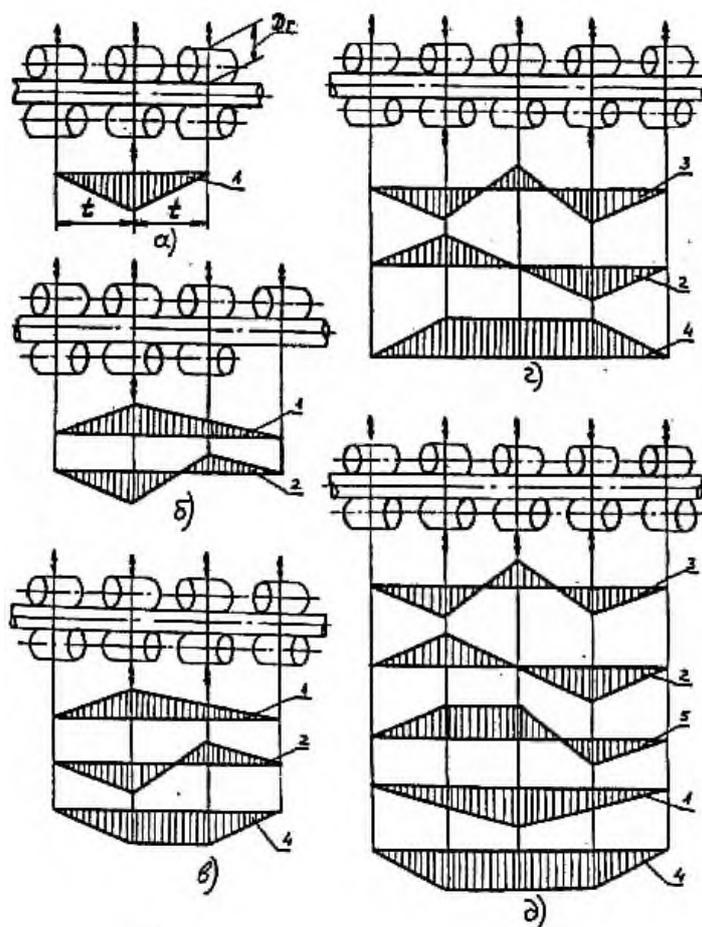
Трубоправильная с двухвалковыми обоймами и валками одинаковой длины (тип ОВ) [4]
